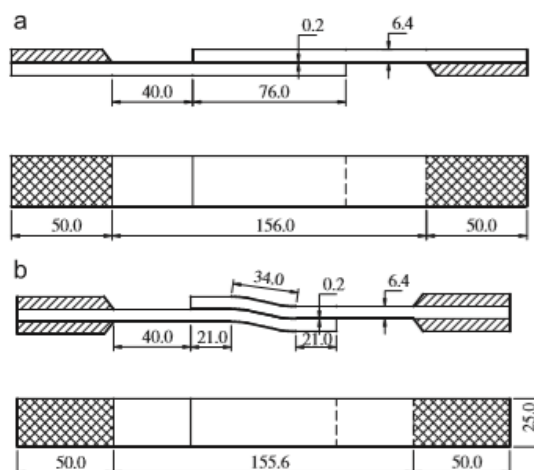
a) Geometria da JSS ensaiada; b) Geometria da junta ondulada ensaiada [46]
